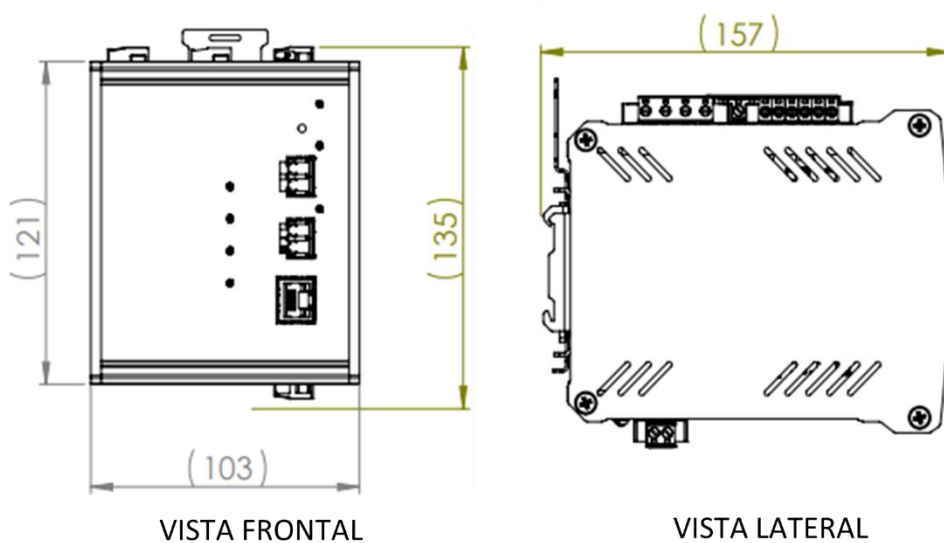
Instalação trilho DIN, vistas frontal e lateral
